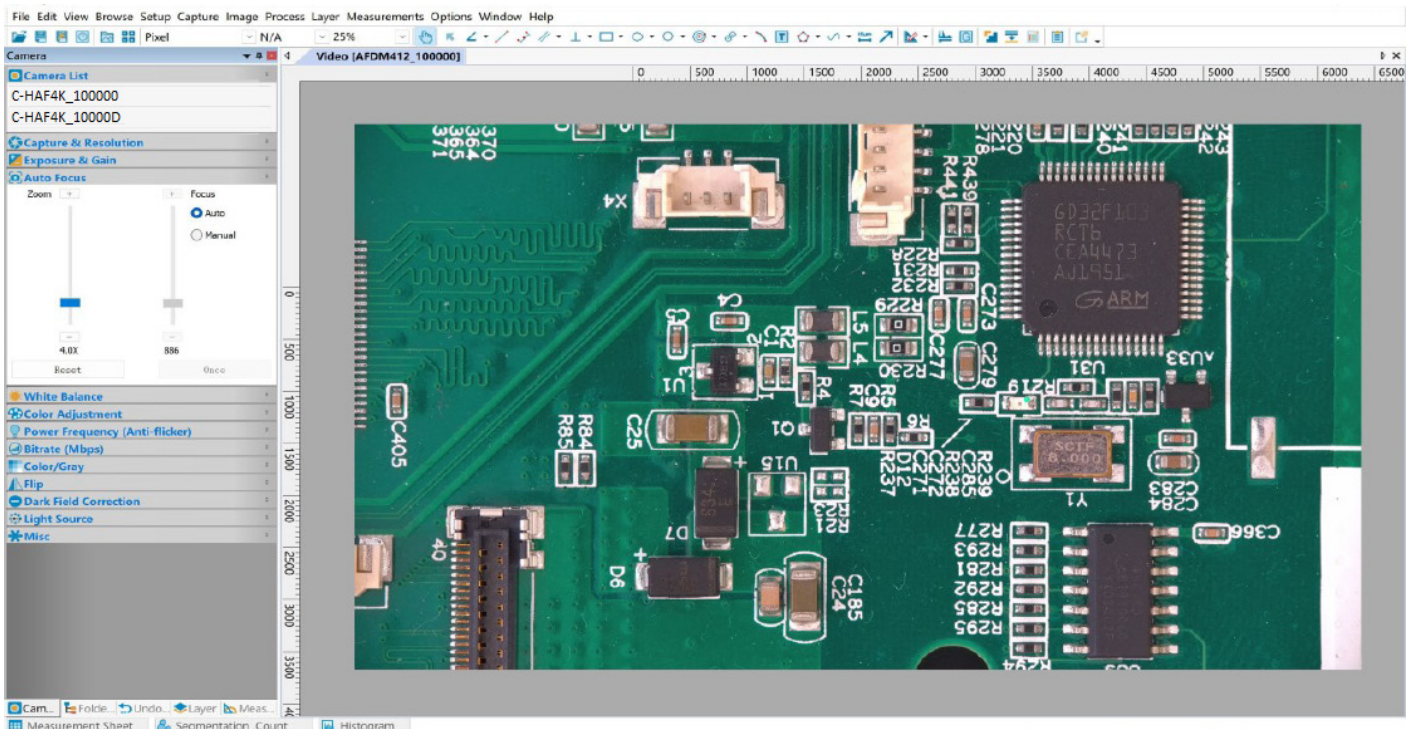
PROVIEW y C-HAF4K Cámaras conectadas en puerto LAN/modo WLAN STA
